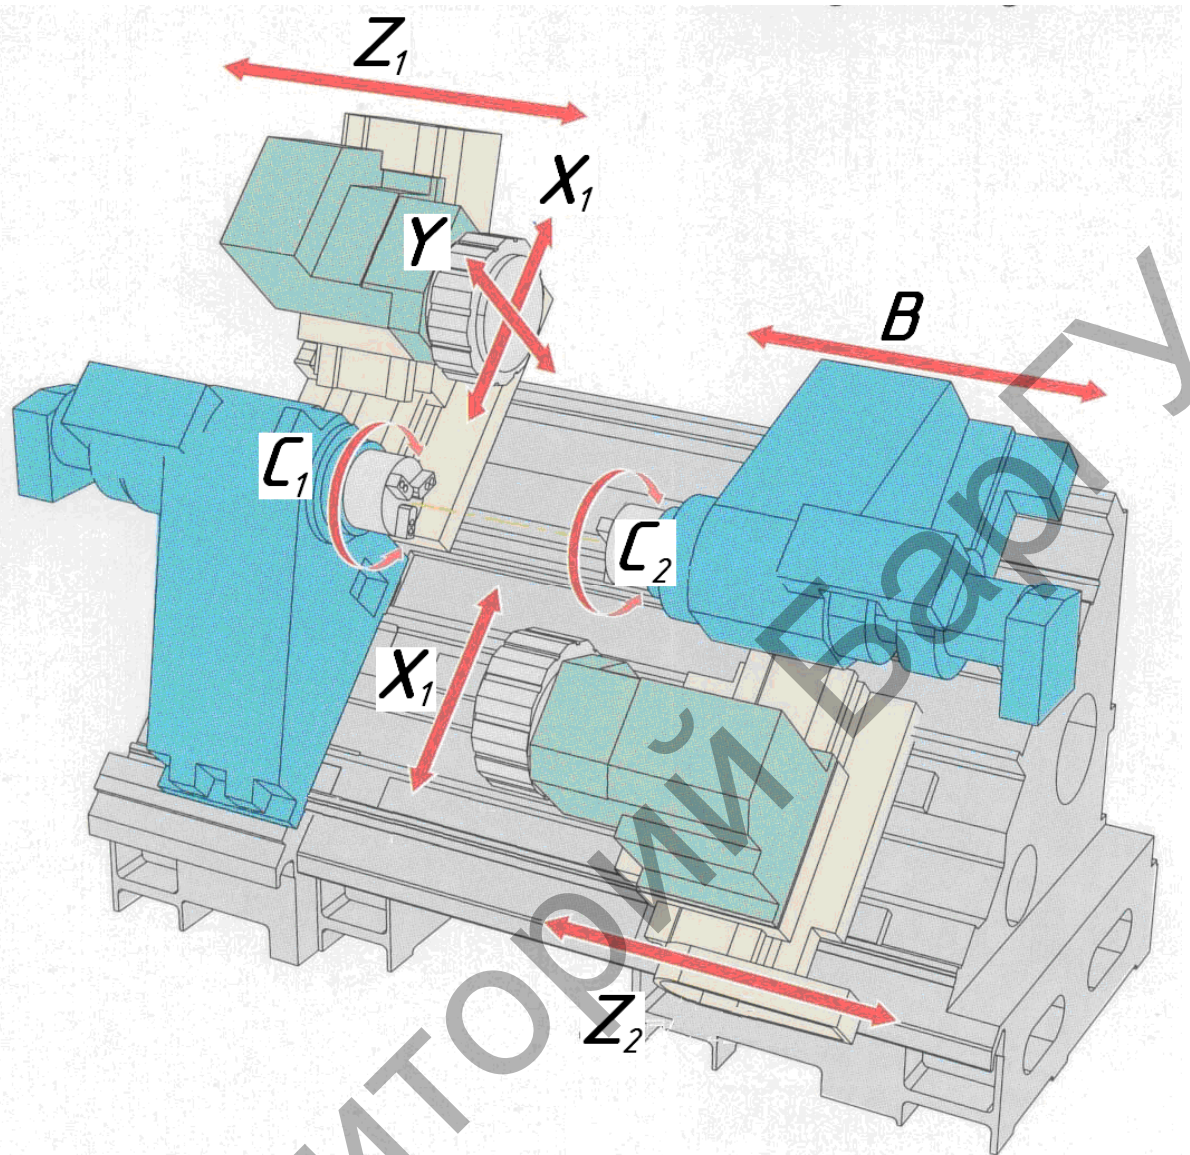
Положение осей у токарного станка с ЧПУ при наличии контршпинделя и двух револьверных головок
